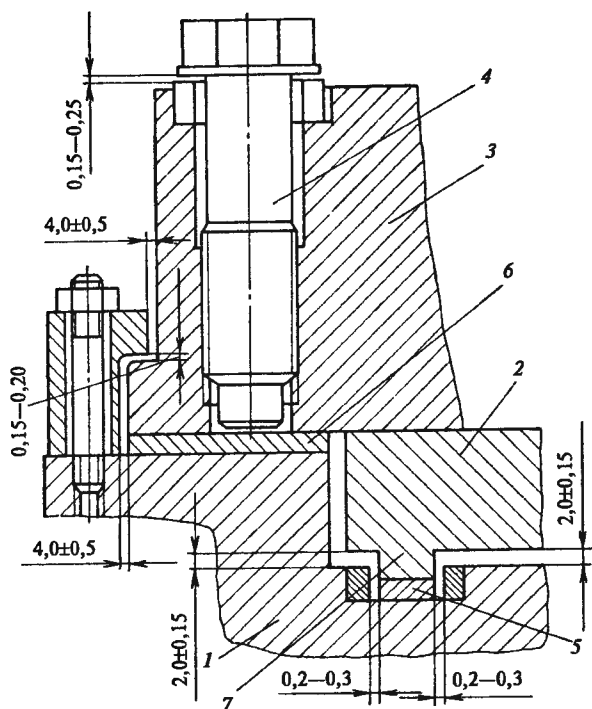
Опираие корпусов ЦВД турбин ХТЗ на корпус подшипника
